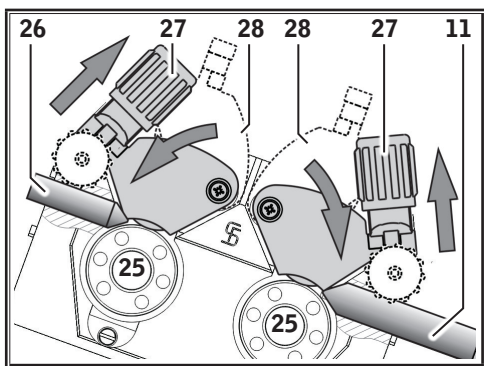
Закрывать 4-роликовый механизм подачи проволоки
